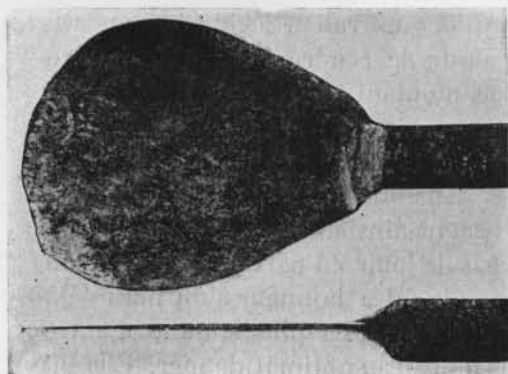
Barre carrée d'acier Bessemer forgée au rouge ordinaire au-dessous de la température de soudage.
